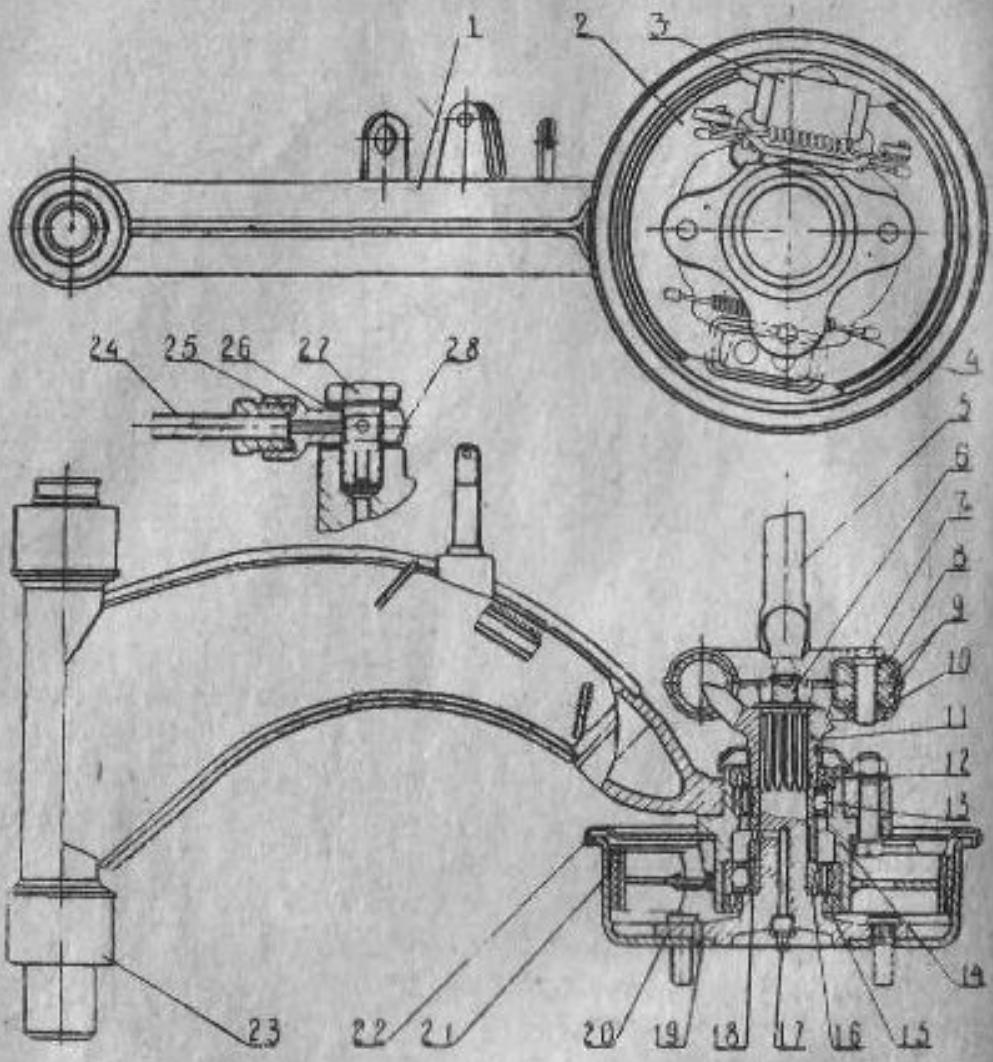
Рычаги, ступицы, привод и тормоза задних колес
